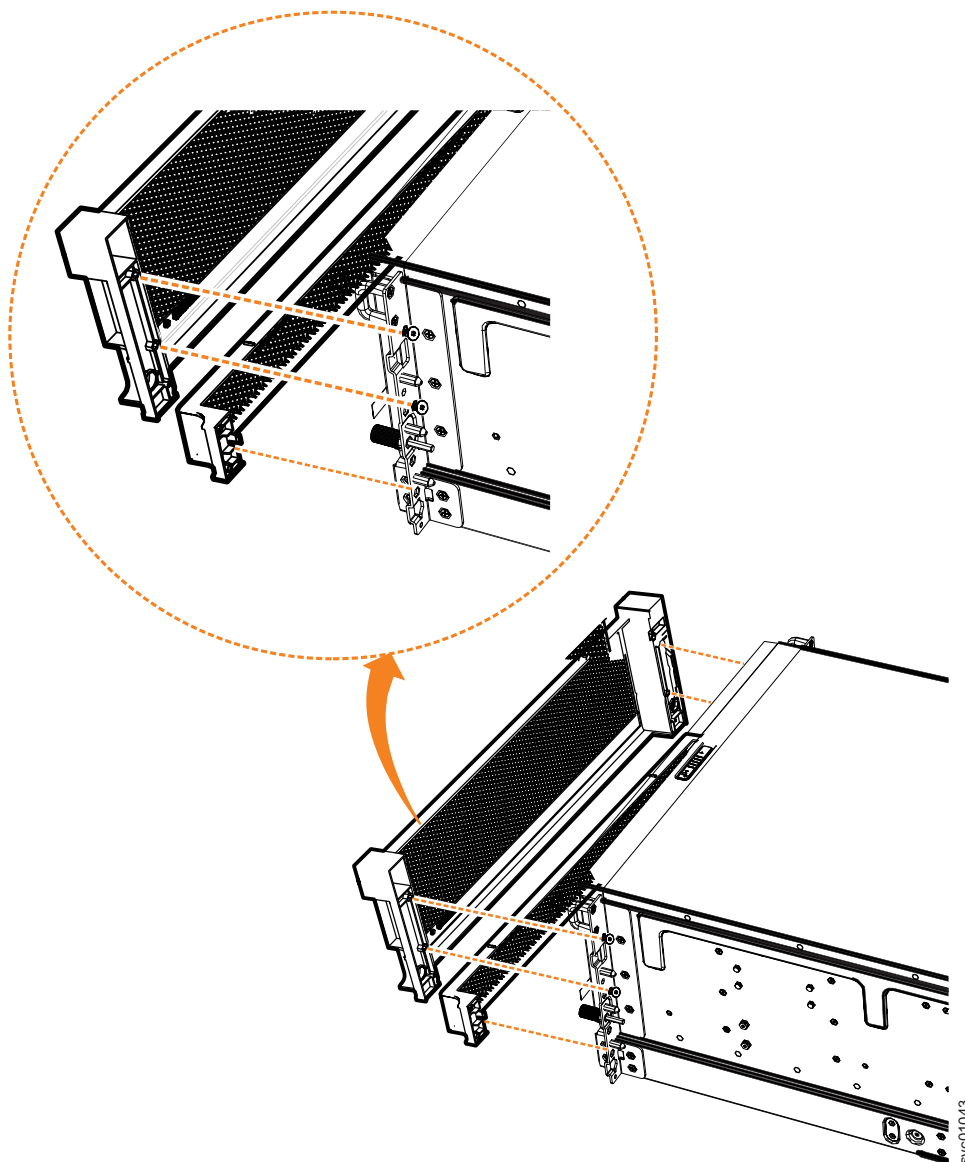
Extraer los componente de carcasa del alojamiento de expansión
